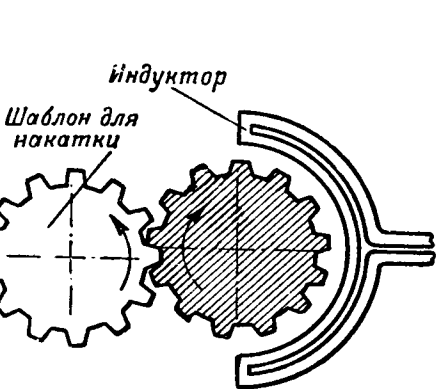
Дуговой индуктор для горячей накатки шестерен.
